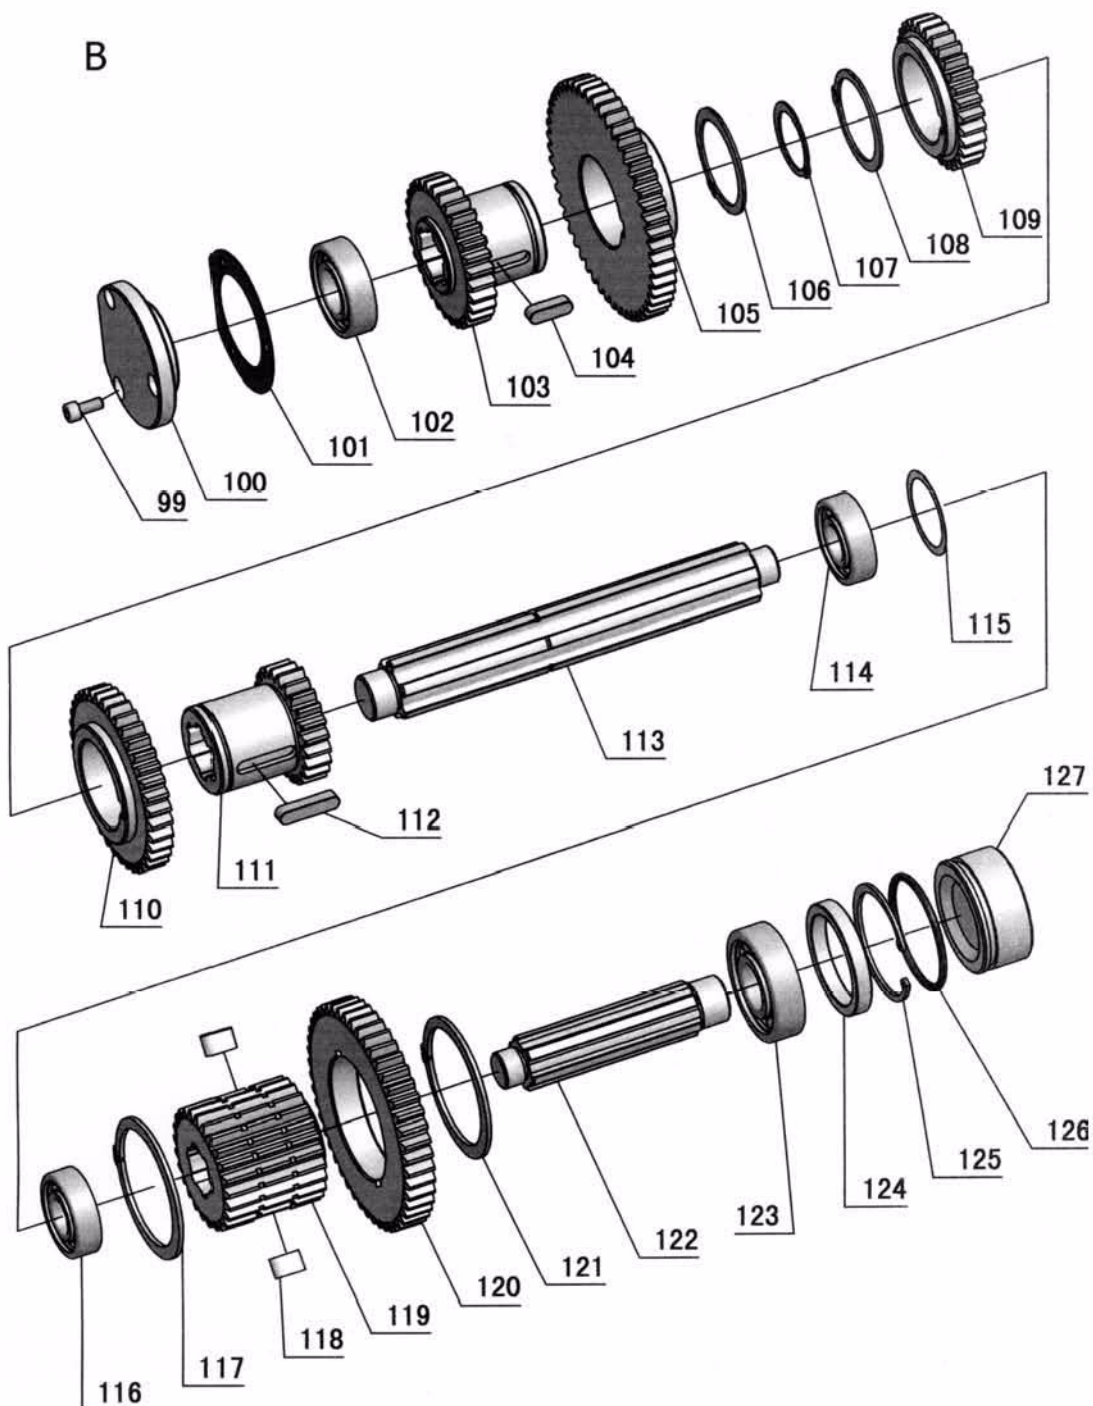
Spindelstock 4 von 8 - Headstock 4 of 8
